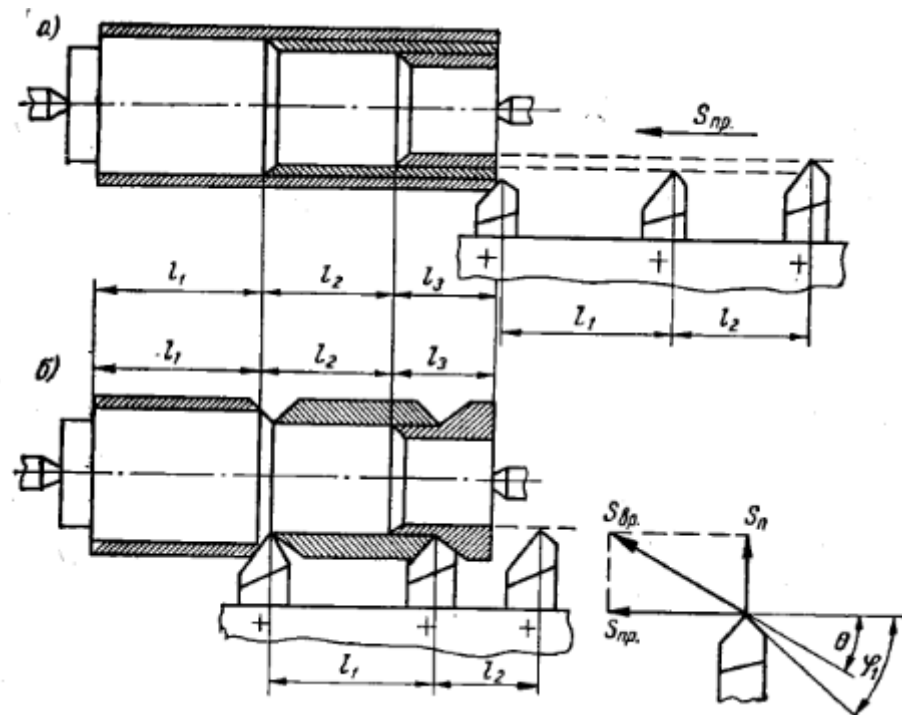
Обробка валу на багаторізцевому верстаті
